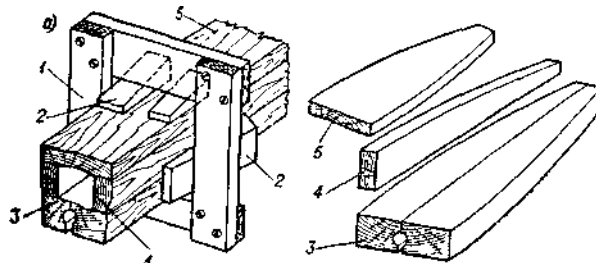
Склеивание мачты: а — приспособление для спрессовки; б — расположение брусков в мачте.
